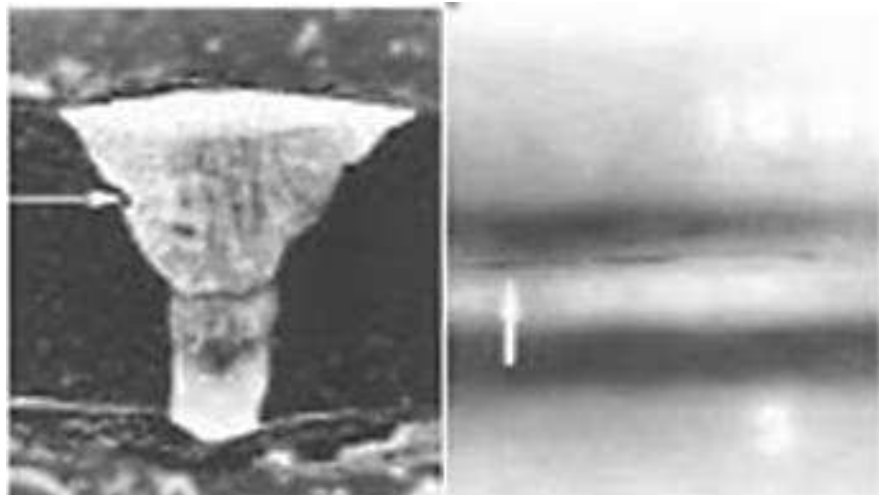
42 *Juntas soldadas con inclusiones de escoria alineadas.
